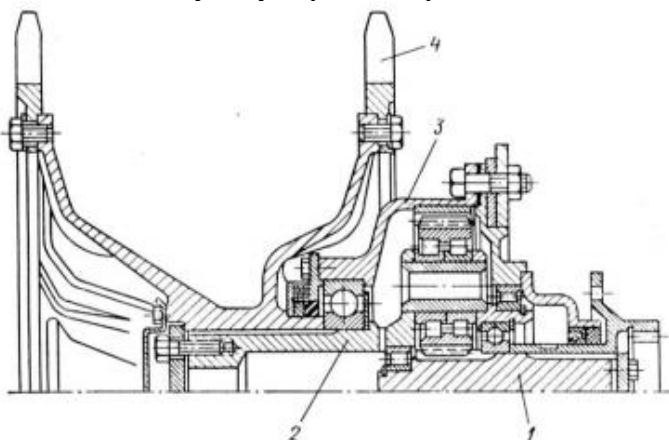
Конструкція однорядної планетарної бортової передачі
